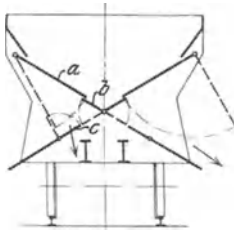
Boden- u. Seitenentleerer der Goodwin Car Co.
